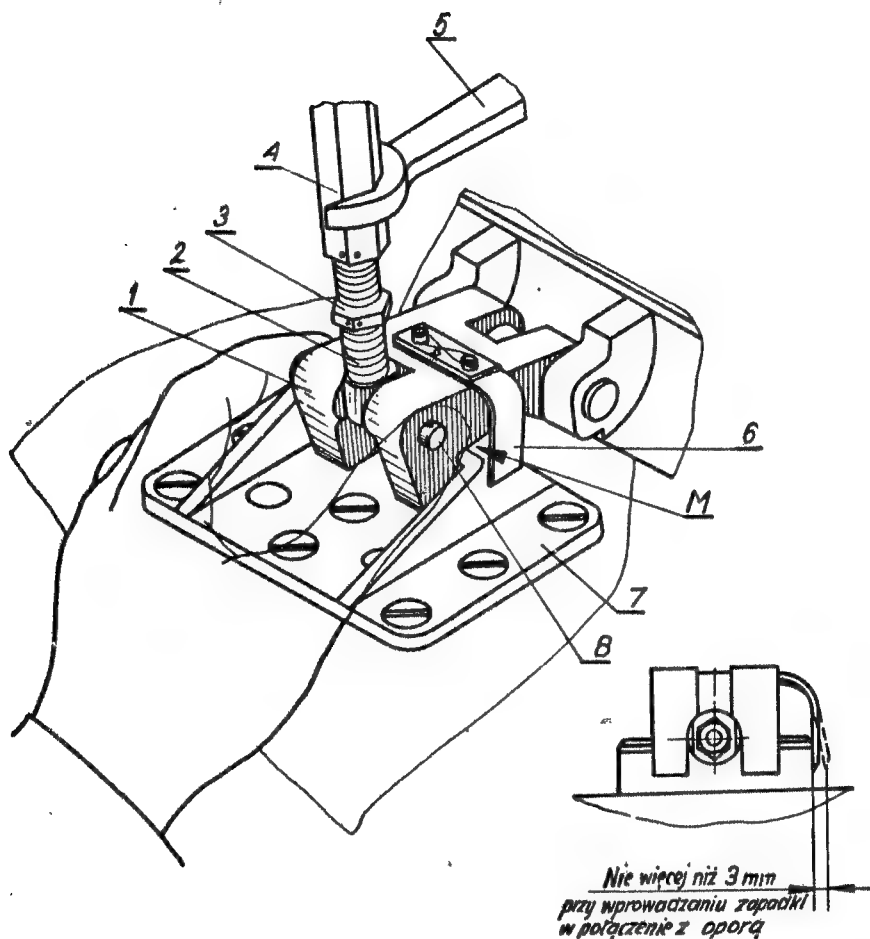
Wkładanie pironaboju w świecę pirotechniczną:
